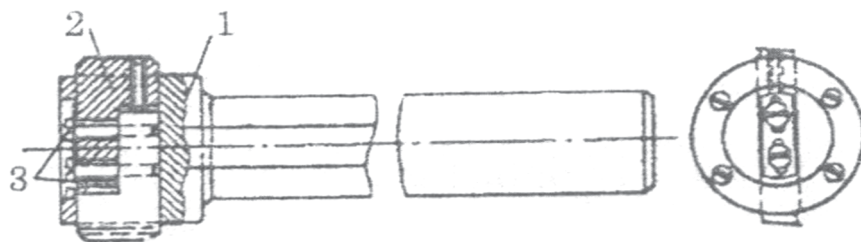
Самоцентрирующая (плавающая) развертка: 1 – корпус; 2 – пластина режущая; 3 – винты фиксирующие
